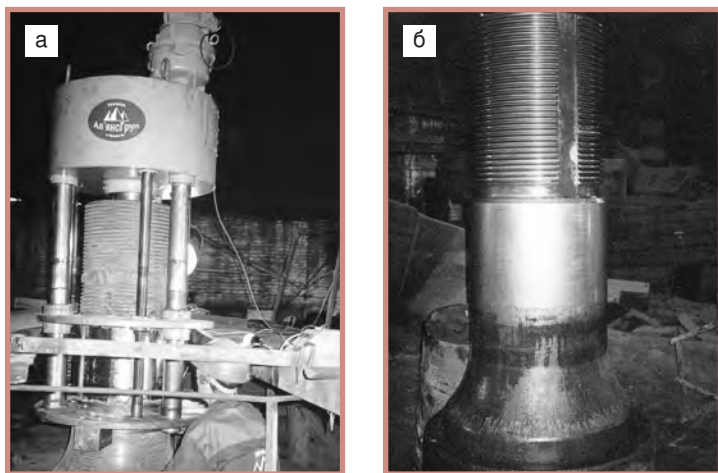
Наплавленный дробящий конус с устройством для механической обработки (а) и внешний вид наплавленного конуса после механической обработки (б)
